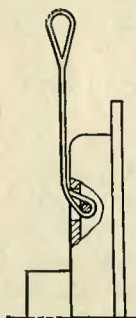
Строповка торцевой крышки с использованием лючка для замера зазоров
